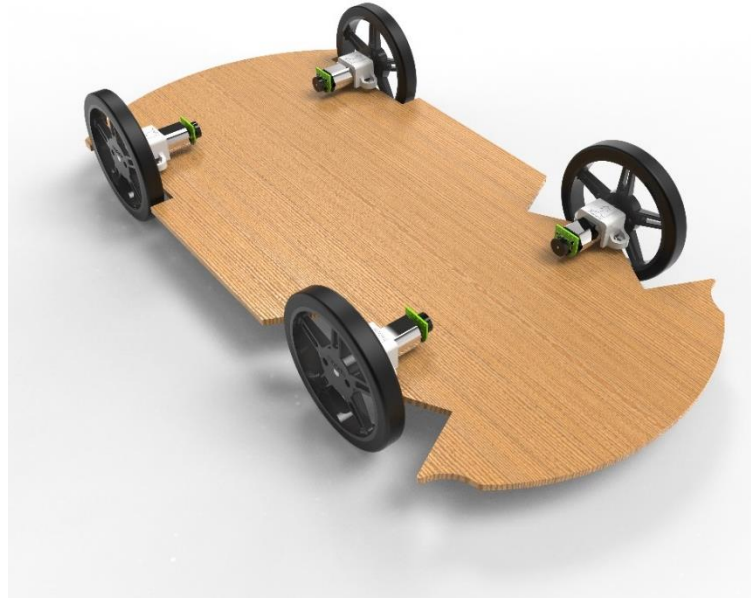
Montagem dos grupos compostos por roda, motor e sensor de velocidade no chassis
